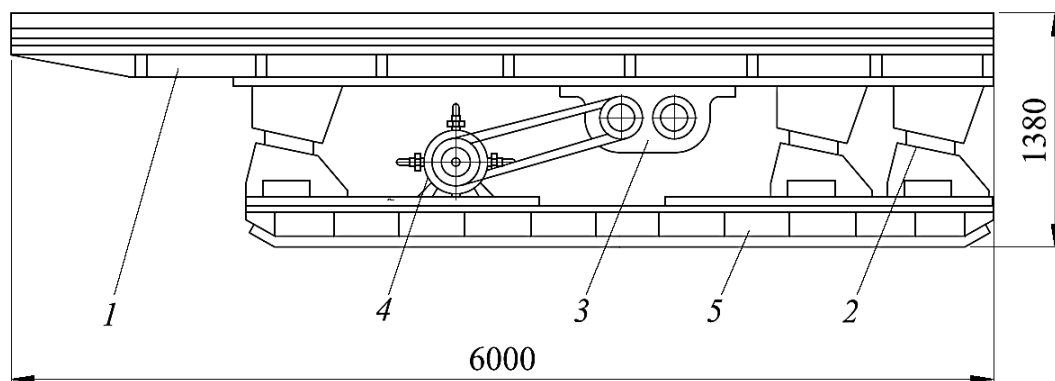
Віброживильник типу ВВДР із пневматичним приводом від роторно-поршневого двигуна об’ємної дії із шарнірно-кулачковим механізмом руху:
